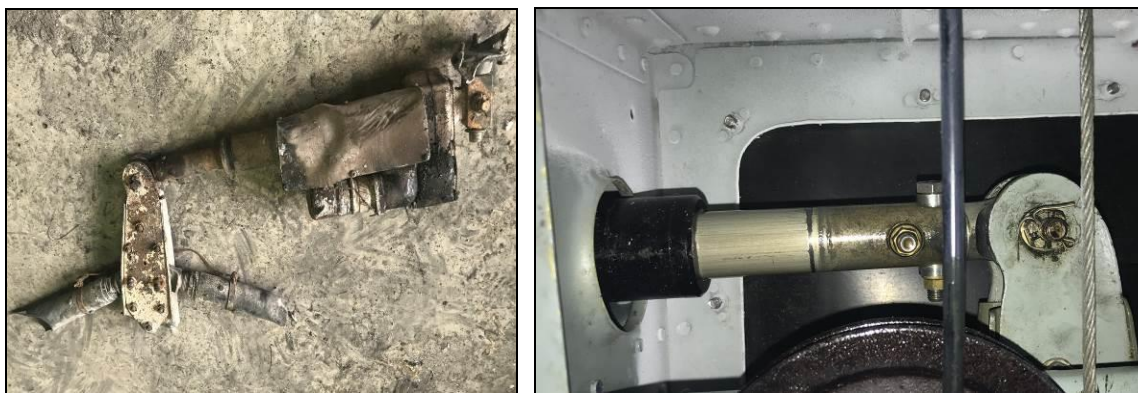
Válvula Principal de combustible del lado izquierdo (Main Fuel Cock).
